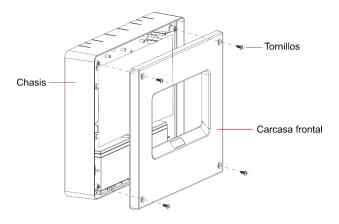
Para abrir la Central CAE-300, retirar los tornillos de la tapa
